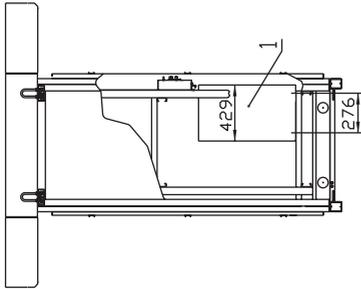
Схема размещения одного выпрямителя В-ОПЕ-М5(М6,М7) (вариант 6)
